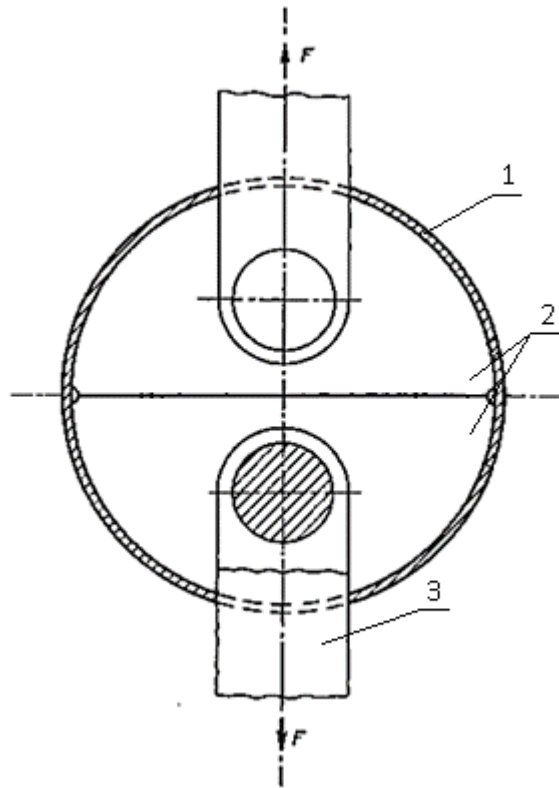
Принципова схема проведення випробування на статичний розтяг зварного кільцевого з'єднання.
